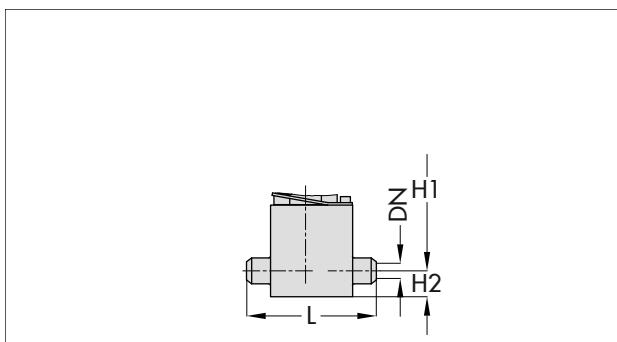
Válvula de paso recto Tipo 3252 con extremos para soldar
